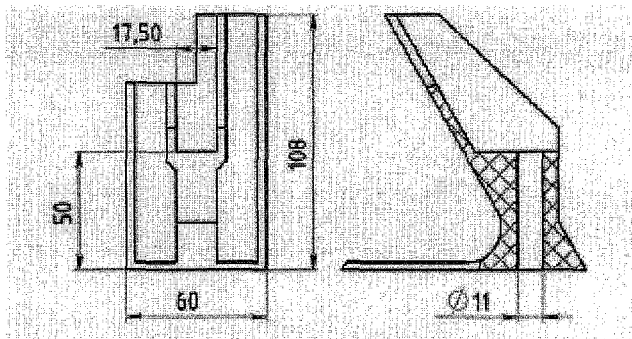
Внешний вид и габаритные размеры крепления УКК-60
